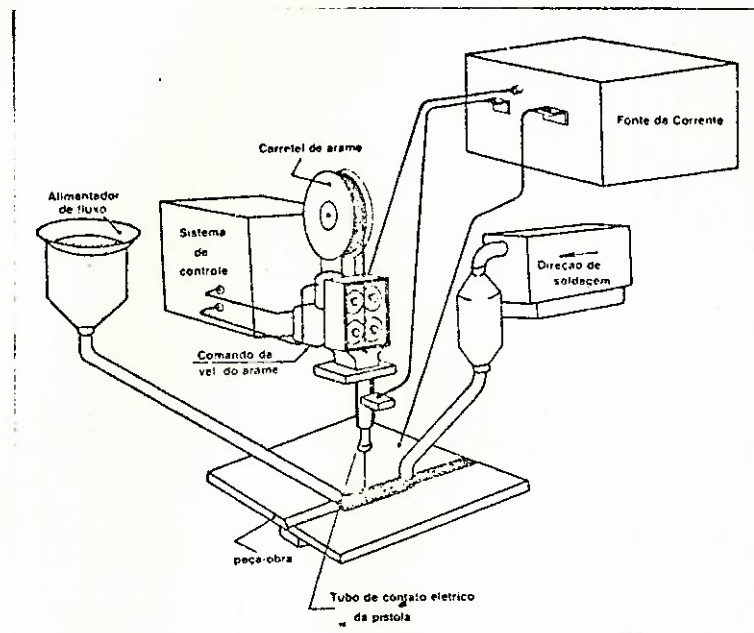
ILUSTRAÇÕES DAS UNIDADES COMPONENTES DO SISTEMA DE SOLDAGEM A ARCO SUBMERSO
